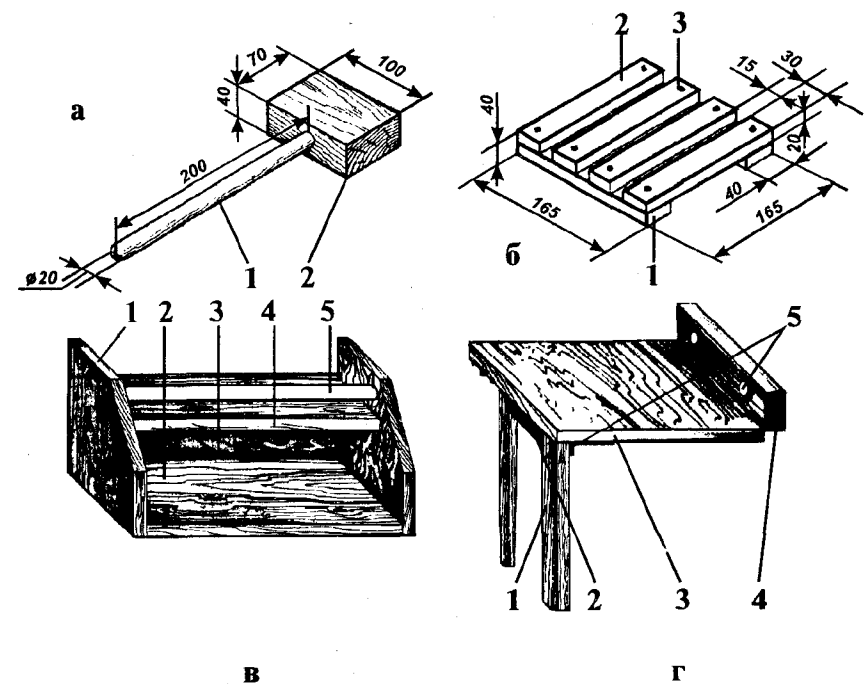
Изделия из древесины, состоящие из нескольких деталей: а — киянка: 1 — ручка, 2 — головка; б — подставка для комнатных растений: 1 — ножка, 2 — рейка, 3 — шуруп (гвоздь); в — полка: 1 — стенка боковая, 2 — основание, 3 — стенка задняя, 4 — полка, 5 — перекладина; г — стол откидной: 1 — ножка, 2 — царга, 3 — крышка, 4 — брусок настенный, 5 — петля
